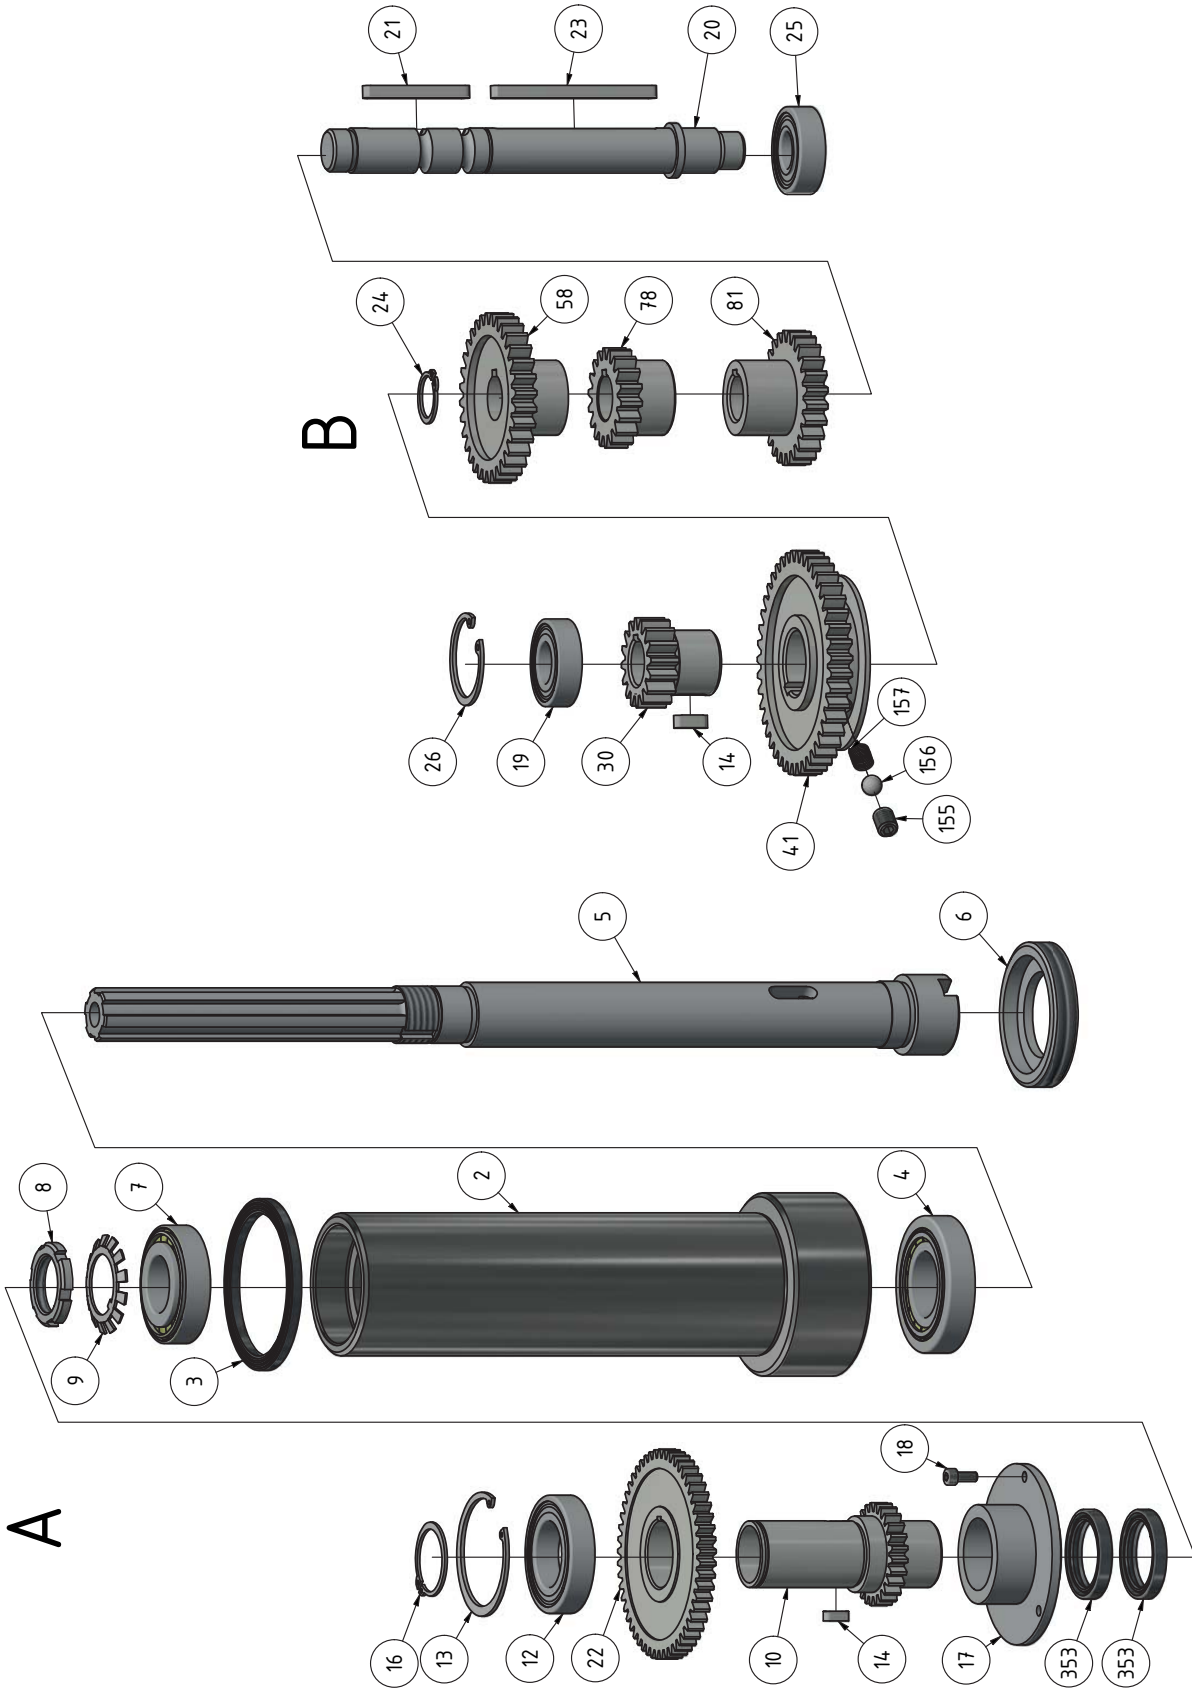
Fräskopf 2 von 6 - Milling head 2 von 6
